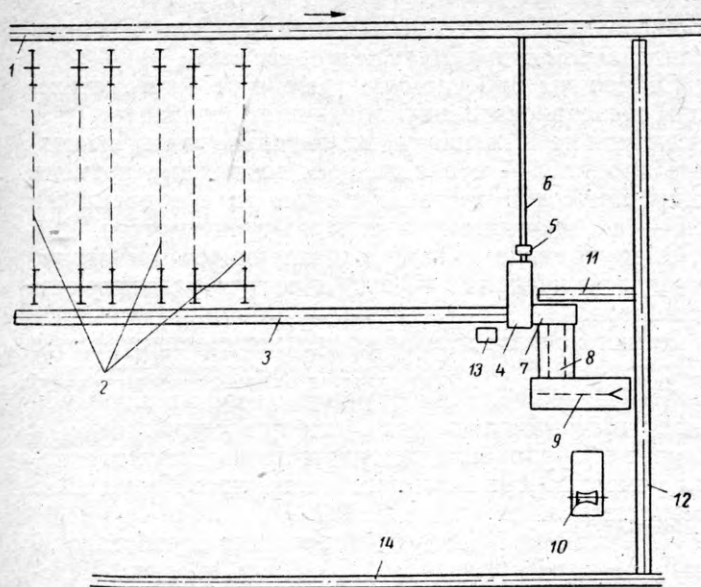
Схема полуавтоматической линии по разделке дров: 1 — сортировочный транспортер Б-22; 2 — буферные горки; 3 — подающий транспортер; 4 — балансирующая пила; 5 — вентилятор; 6 — пневмопровод; 7 — приемный стол с двухсторонним сбрасывателем; 8 — синхронизатор; 9 — цепной колуна; 10 — станок для окорки осинового баланса; 11 — транспортер для нерасколотых дров; 12 — выносной транспортер; 13 — пульт управления; 14 — разгрузочный транспортер.
